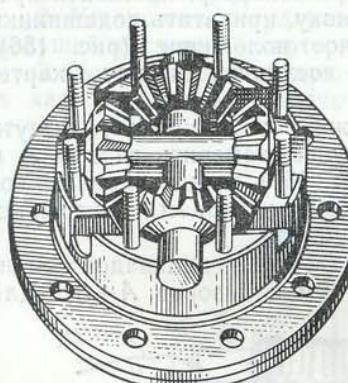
Установка крестовины с сателлитами и шайбами в левую коробку сателлитов
